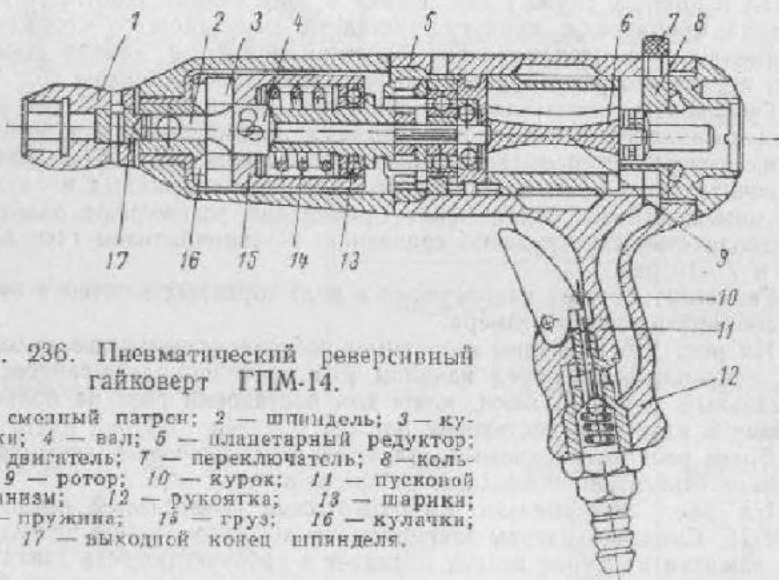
Пневматический реверсивный гайковерт ГПМ-14.
